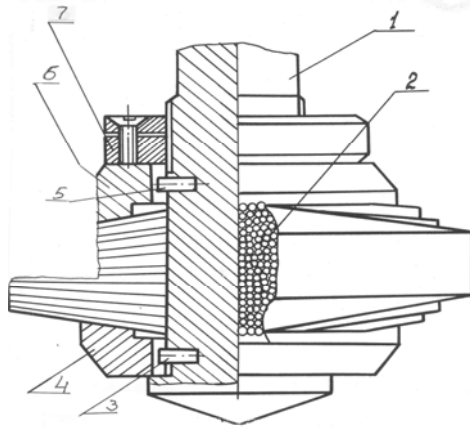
Конструкція ріжучого колеса, виготовленого у вигляді голкофрези
